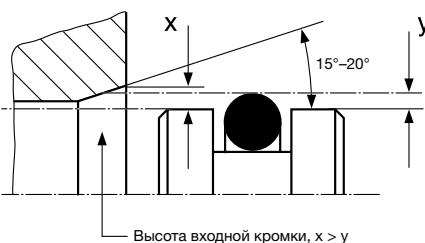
На схеме показана фаска входной кромки и уплотнительное кольцо перед сжатием. Размер «*x*» должен быть больше размера «*y*» для обеспечения сборки без помех.
